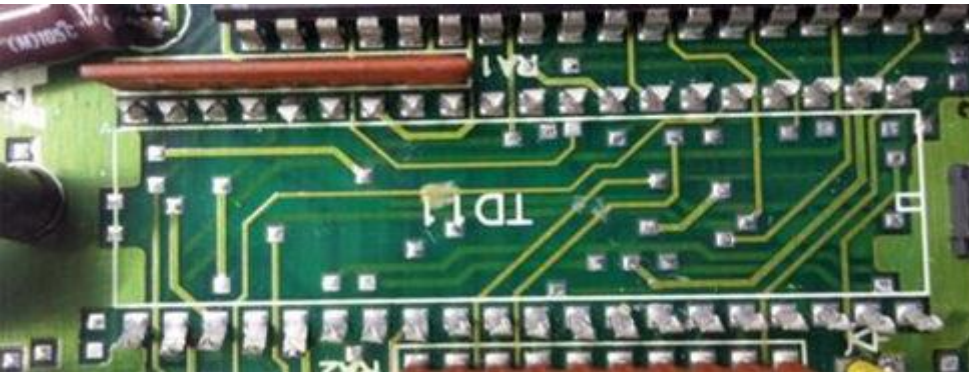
Entegre bacaklarının keski ile kesilmesi.
